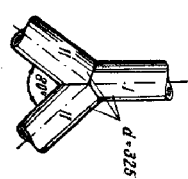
Сварной тропинка разветвленной (штаны).
